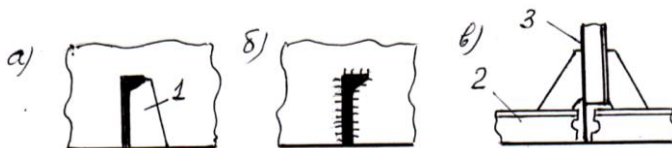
Соединение продольных балок на водонепроницаемых переборках:
